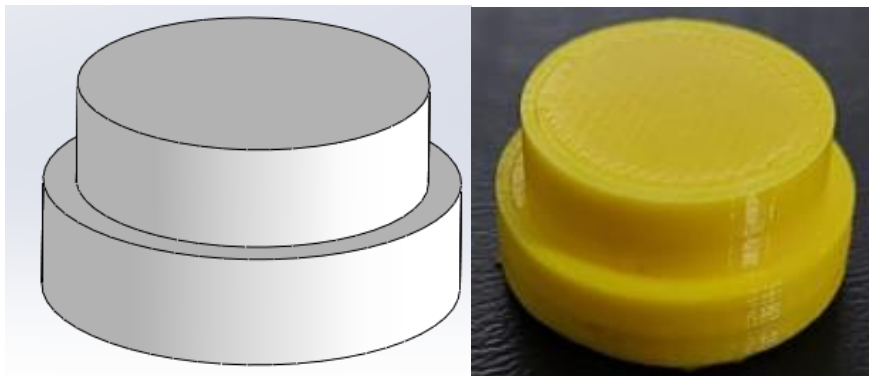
Segmento de ensamble de tornillo sinfín en CAD e impreso.
